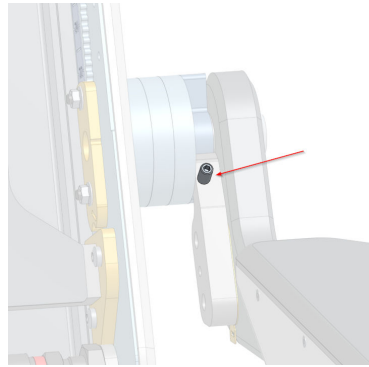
Vis de réglage pour régler l'angle de l'accoudoir
